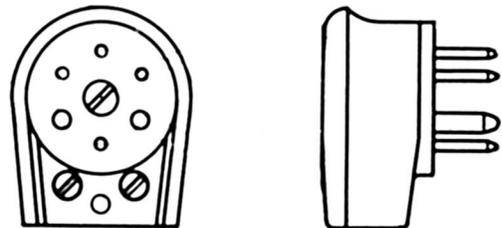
Befestigung des sechspoligen Einbausteckers auf dem Aggregat WR 400.
